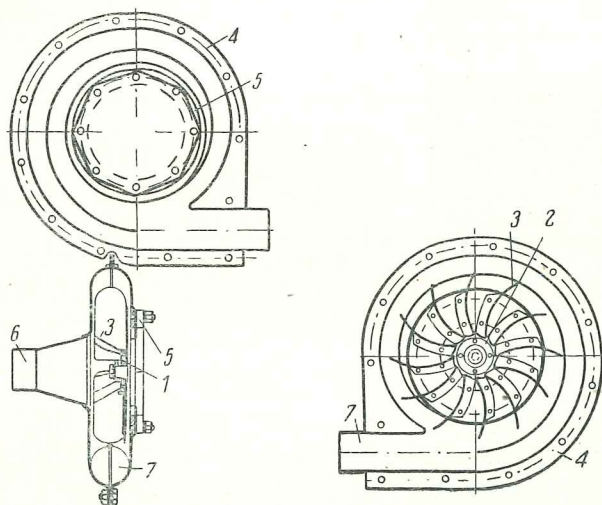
Схема центробежного вентилятора установки ЗИС-13:
